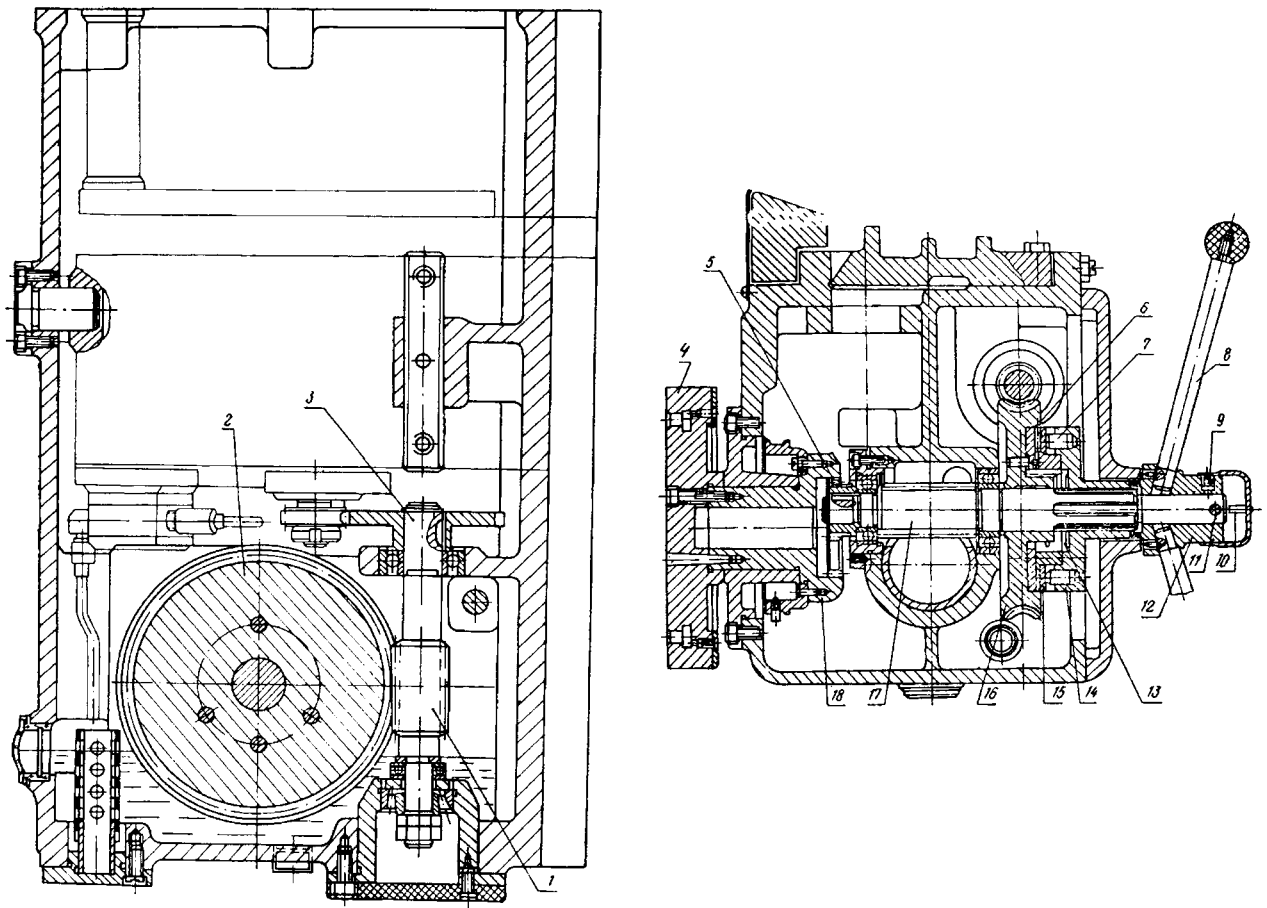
Механізм подач шпинделя свердлильного верстата 2Н118-1
